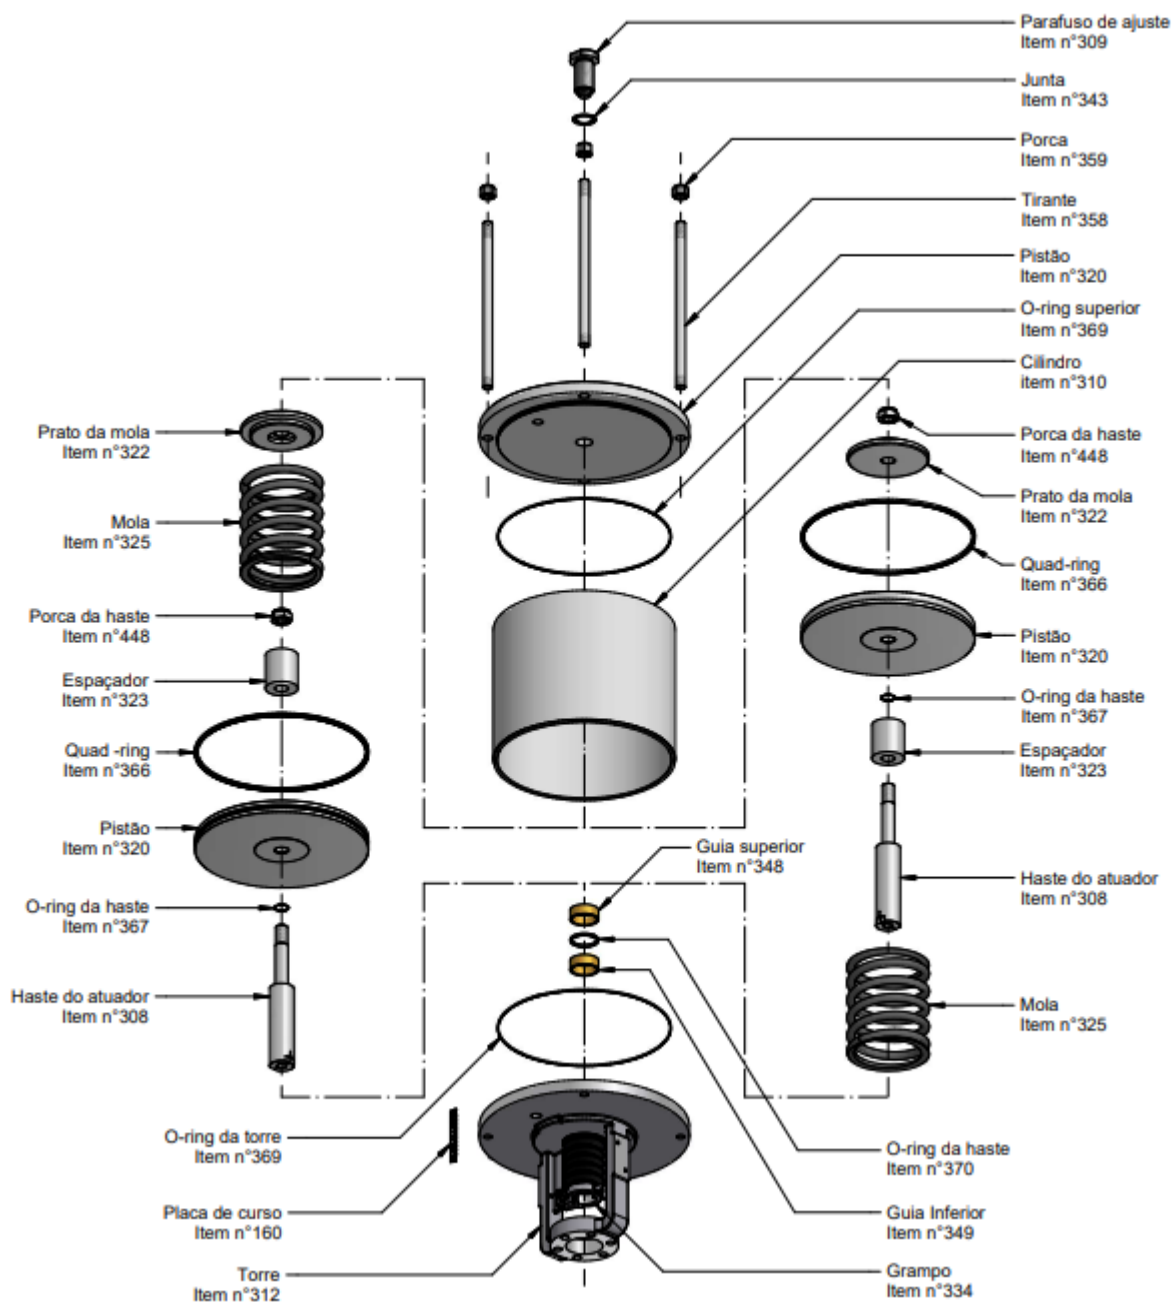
Vista Explodida do Sub. Conjunto do Atuador
